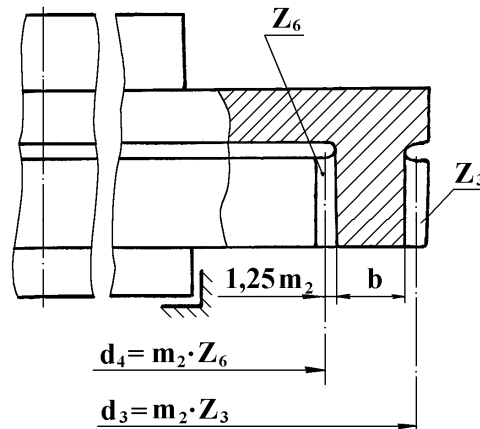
Розрахункова схема для визначення числа зубів підциліндрового зубчастого колеса
